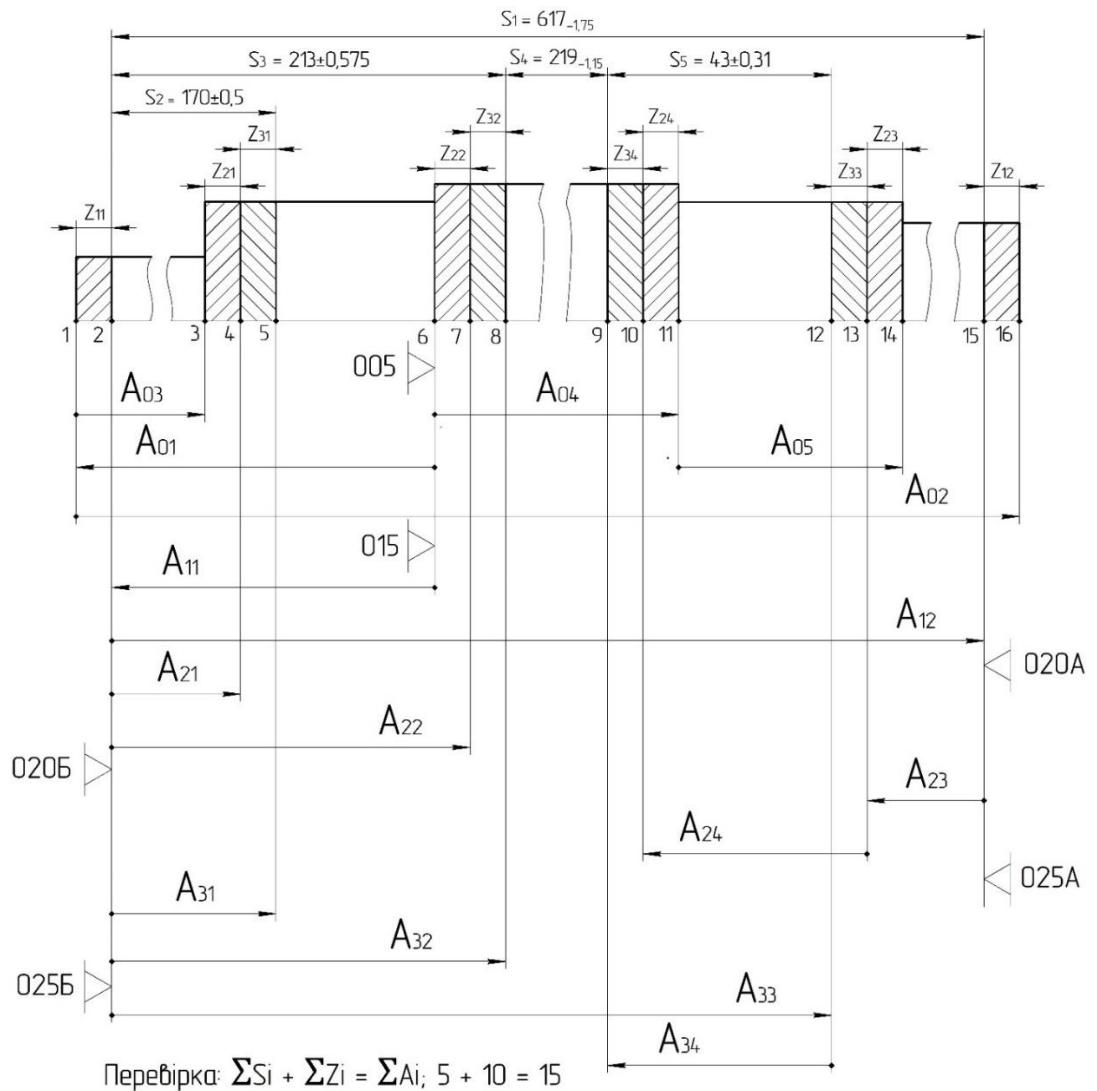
Схема обробки торцевих поверхонь вала
